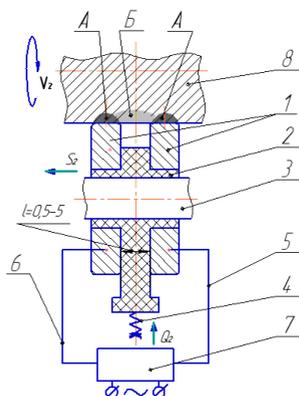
Схема двухинструментального способа ЭМПЗ
